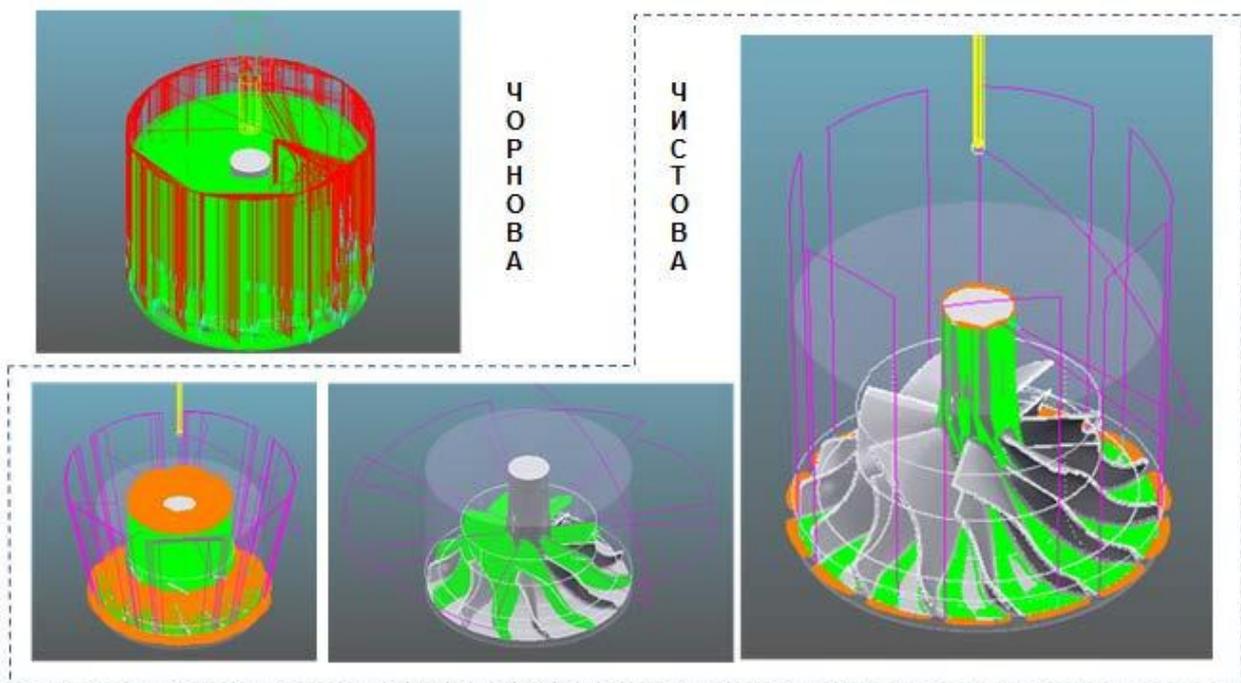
Траєкторії чорнової та чистової обробки заготовки.
